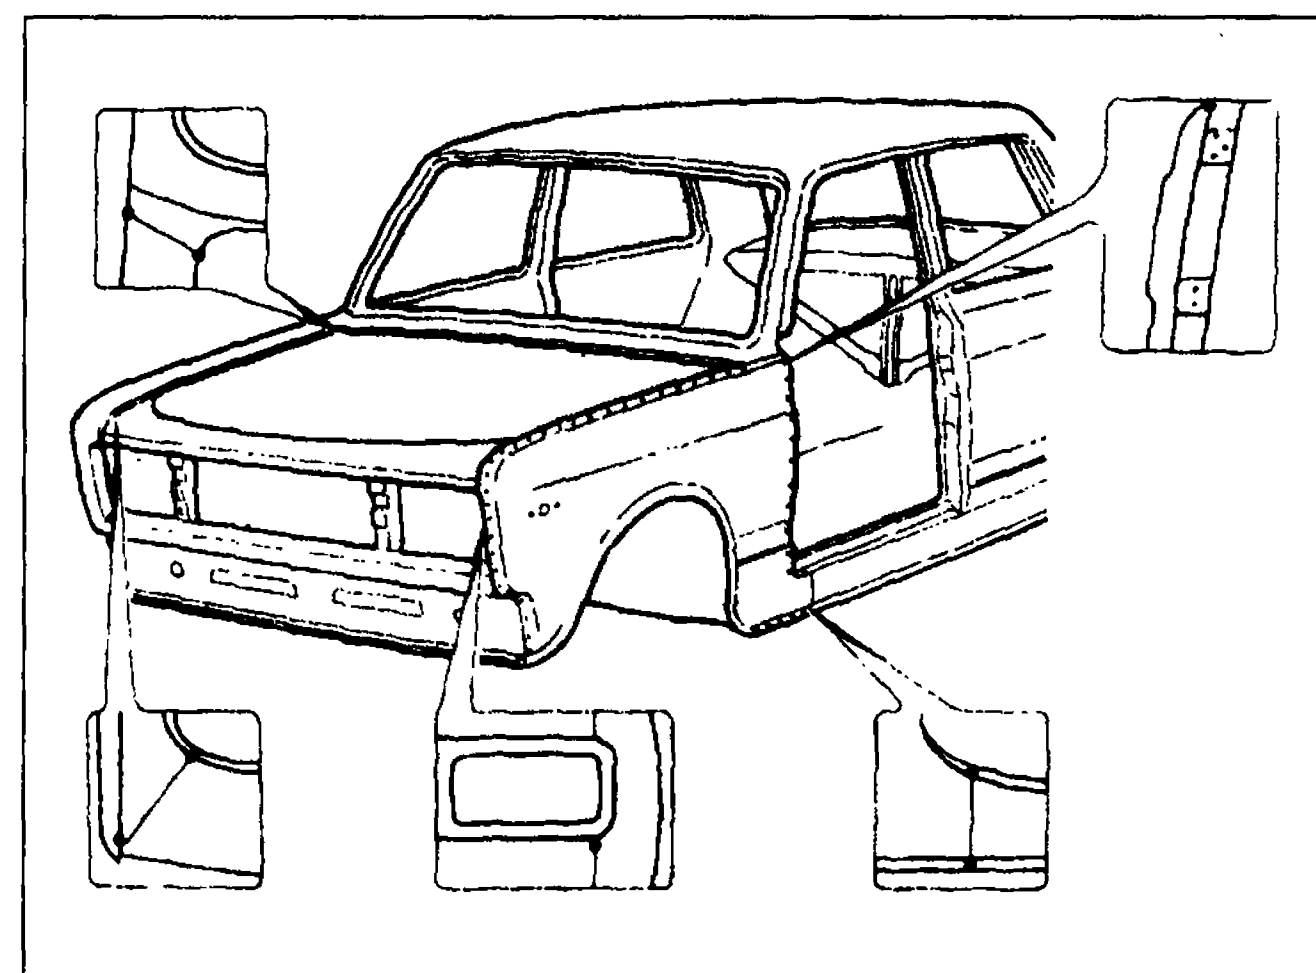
Места сварки переднего крыла. На основном виде точками обозначены швы контактной сварки. На фрагментах показаны точки газовой сварки.
